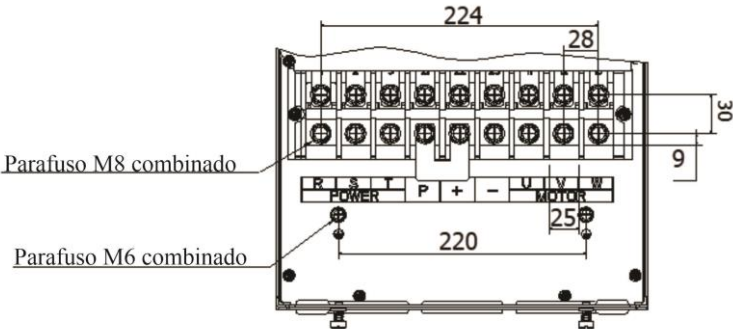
Terminal circuito principal 75kW G3/F3 (Chassis No.: A8)
